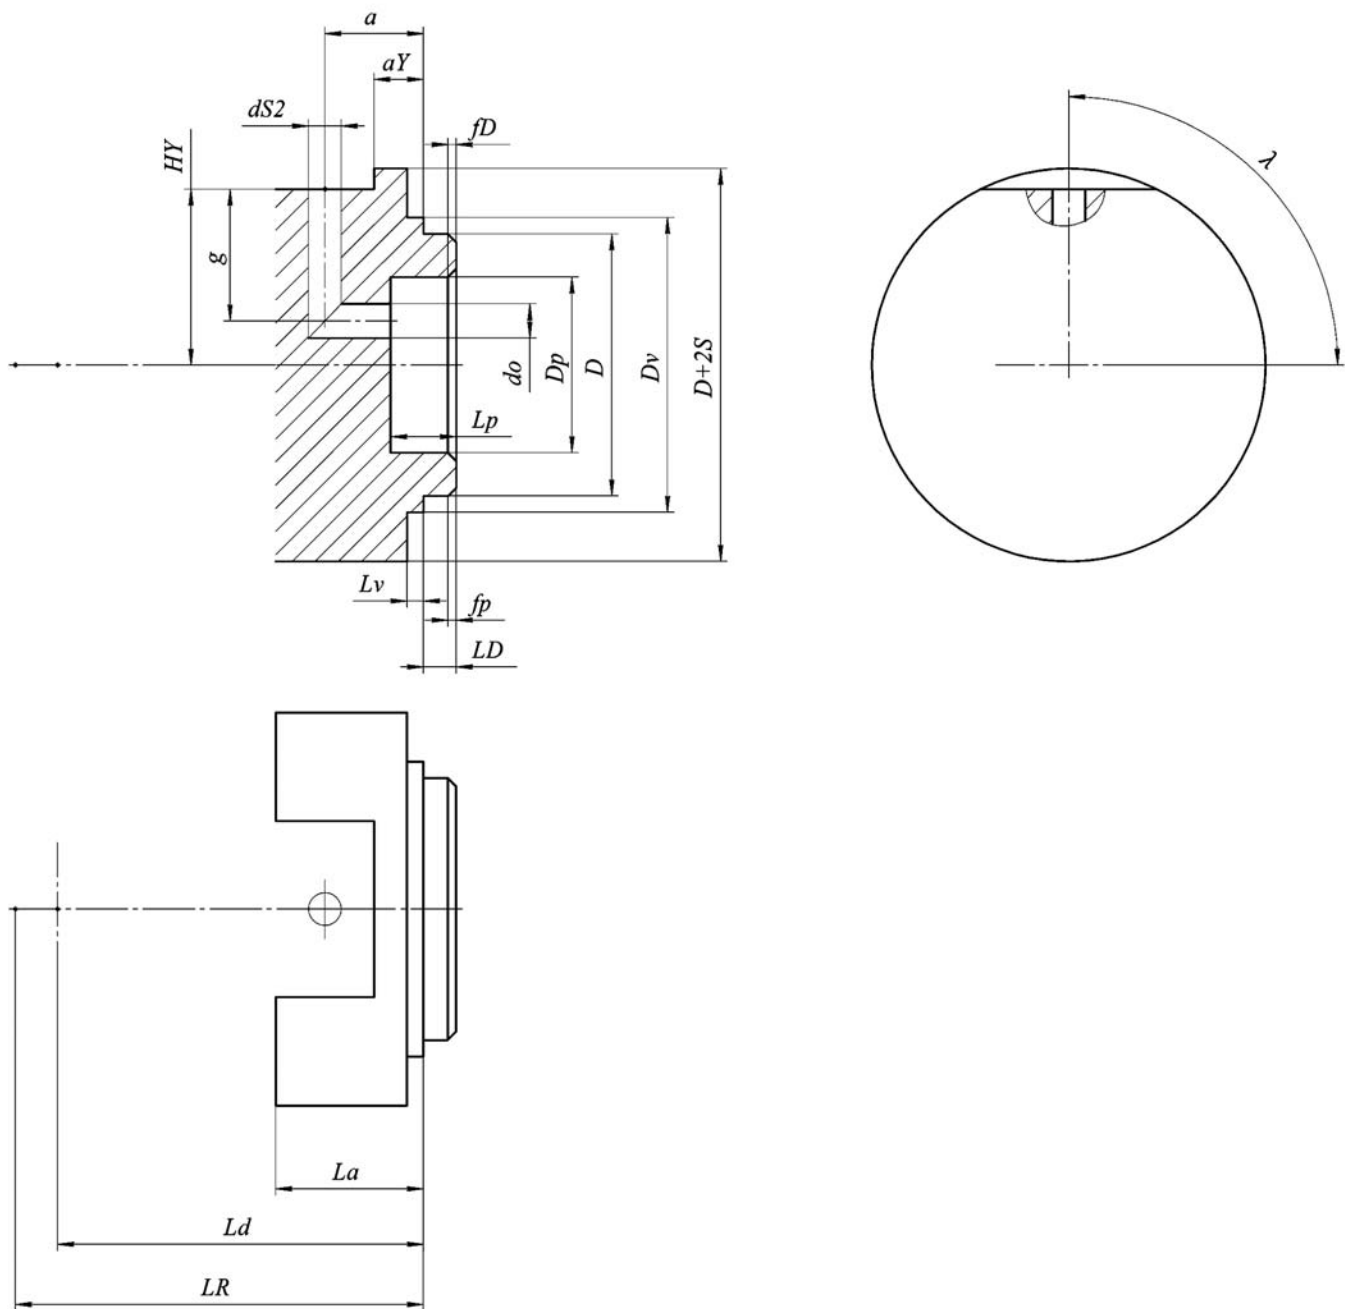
Параметризованный эскиз присоединительной части крышки задней
